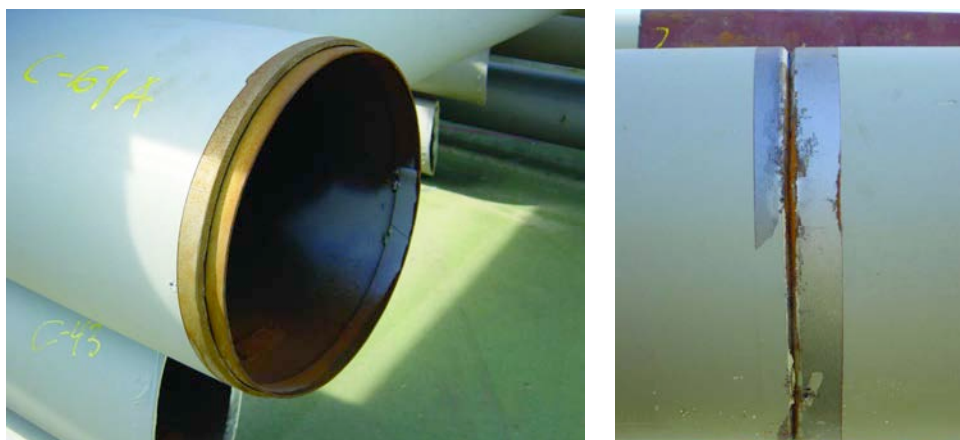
Soldaduras en línea. Preparación de la camisa y unión.
